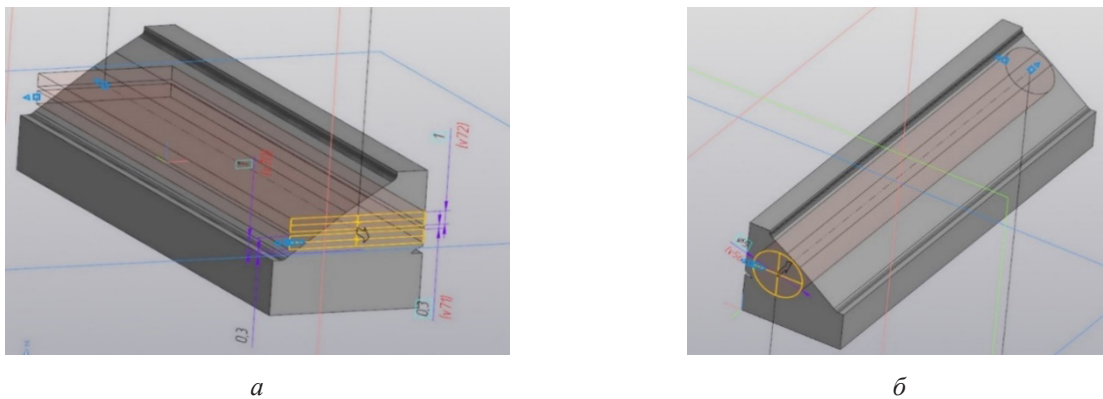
Схема вырезки образцов из сварного шва уторного узла
